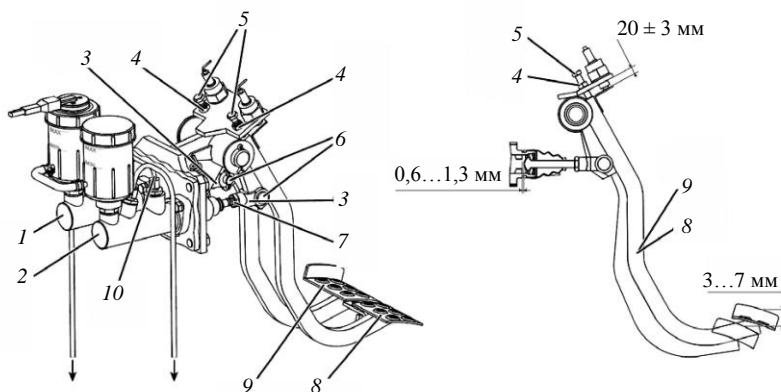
Регулировка рабочих тормозов: 1, 2 – гидроцилиндры; 3 – вилки; 4, 7 – контргайки; 5 – регулировочные болты; 6 – пальцы; 8, 9 – педали; 10 – клапан
